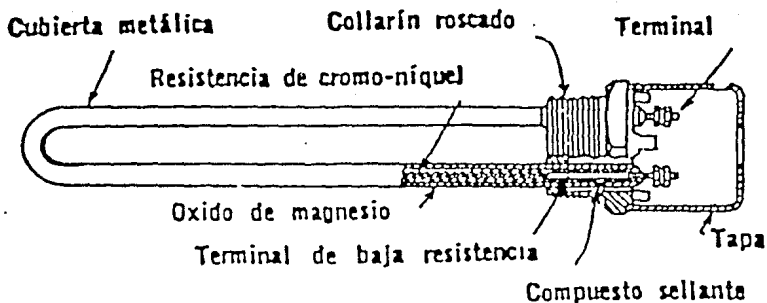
VISTA SECCIONAL DE UN CALENTADOR DE
